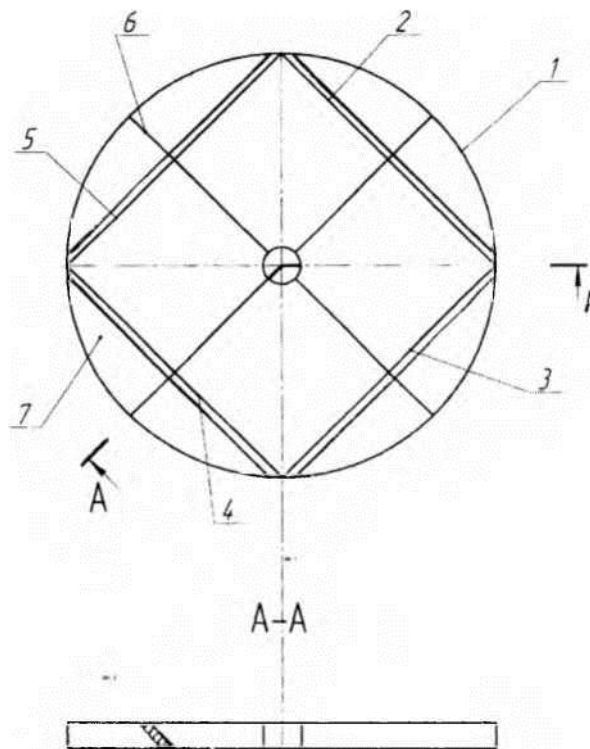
Робочий орган [], вид зверху і переріз А-А
